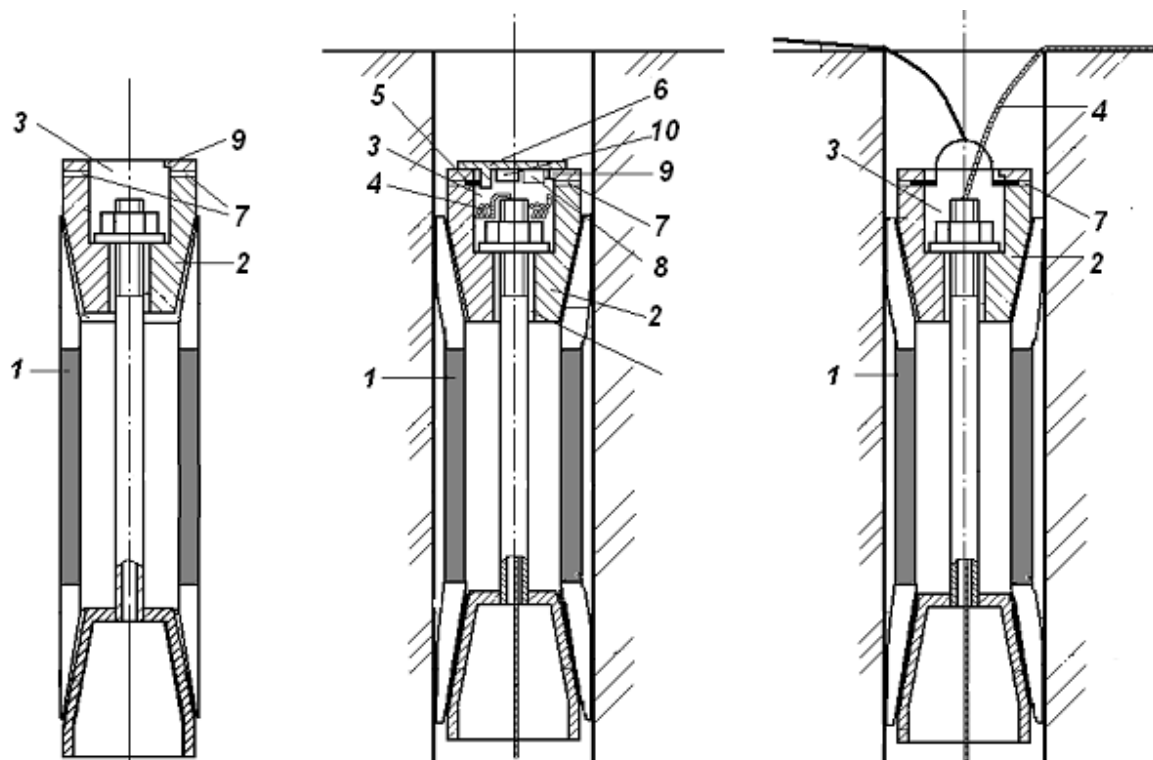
Схема металлической забойки с локализатором взрывной сети:
